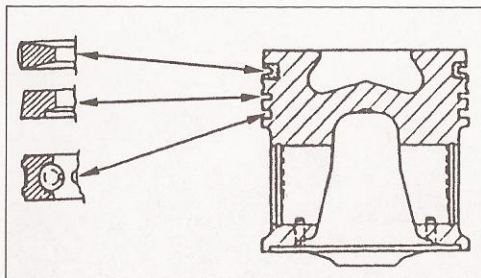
Расположение поршневых колец на поршне (двигатели 8040.25 и 8060.25)
